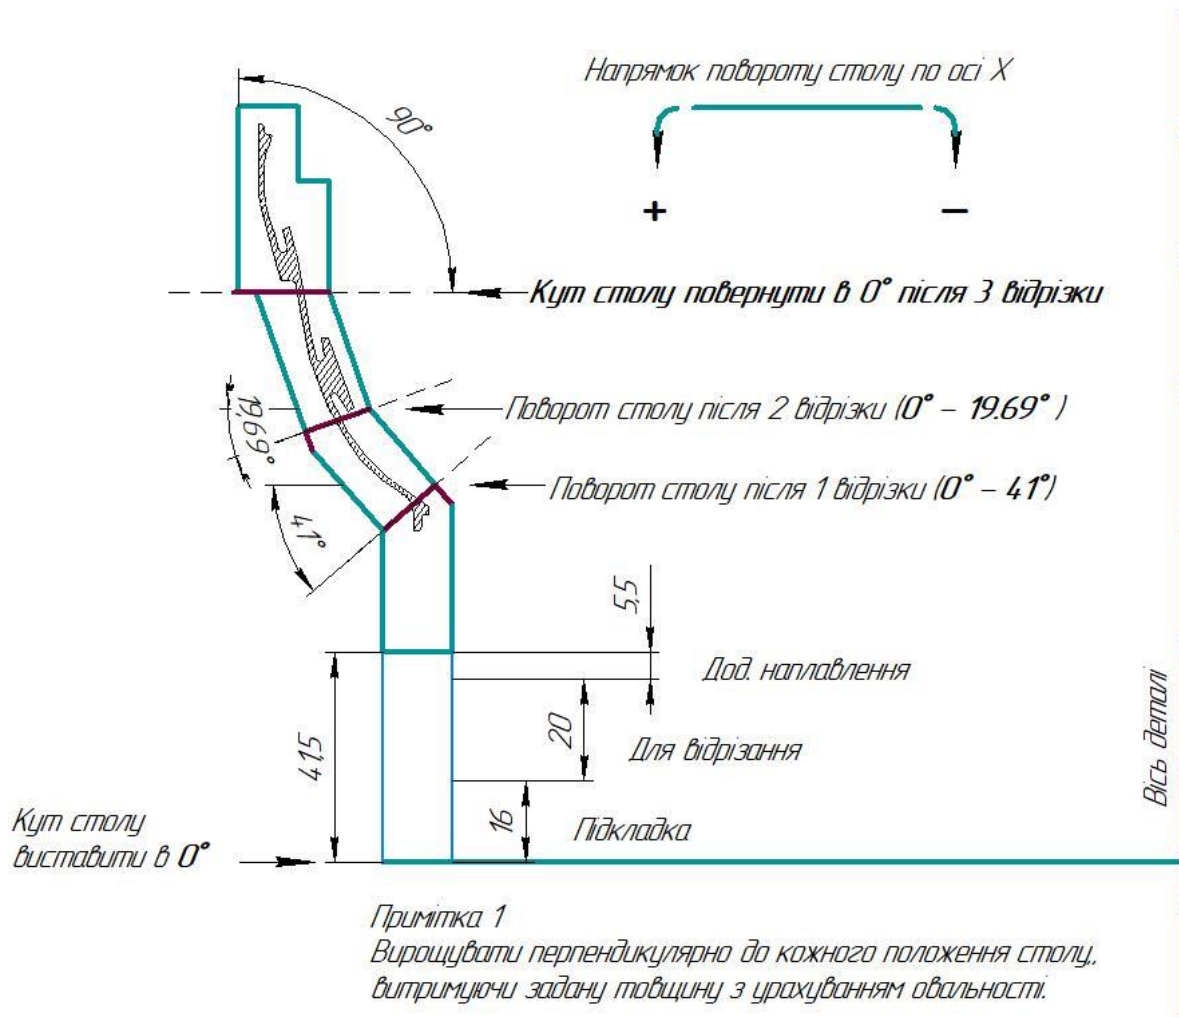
Креслення повороту столу для наплавлення деталі 4500301001 (Зроблено в КОМПАС-3D v17).
